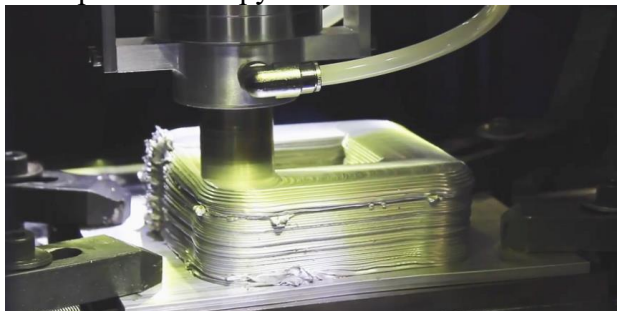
3D-печать ротационной сваркой трением
